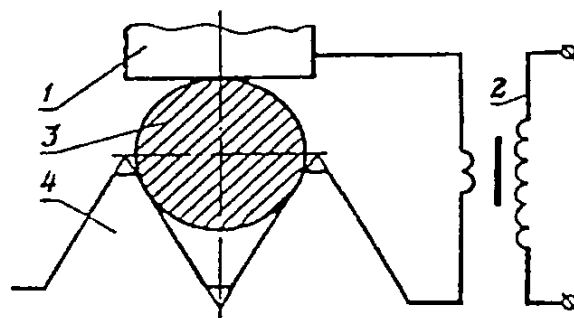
Электроконтактная приварка проволоки к виткам резьбы: 1 – электрод; 2 – сварочный трансформатор; 3 – присадочная проволока; 4 – витки резьбы
